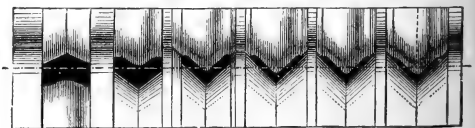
Walzen für gleichschenkeliges Winkelisen.
